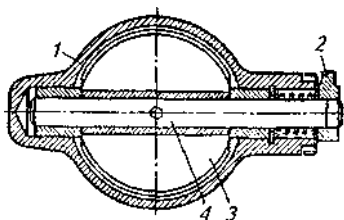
Моторный тормоз-замедлитель: 1 — корпус; 2 — поворотный рычаг; 3 — заслонка; 4 — вал
